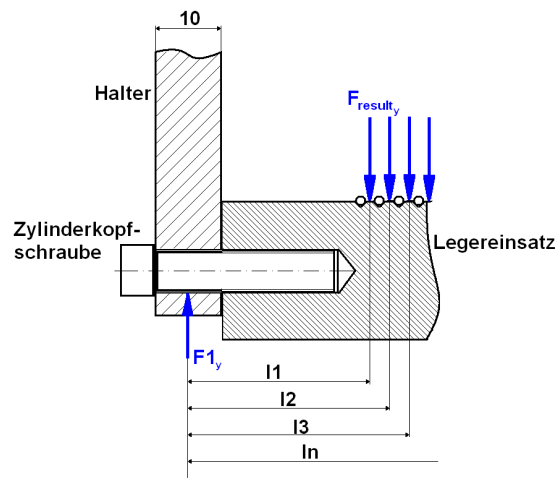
Befestigung des Legereinsatzes mit Schrauben
